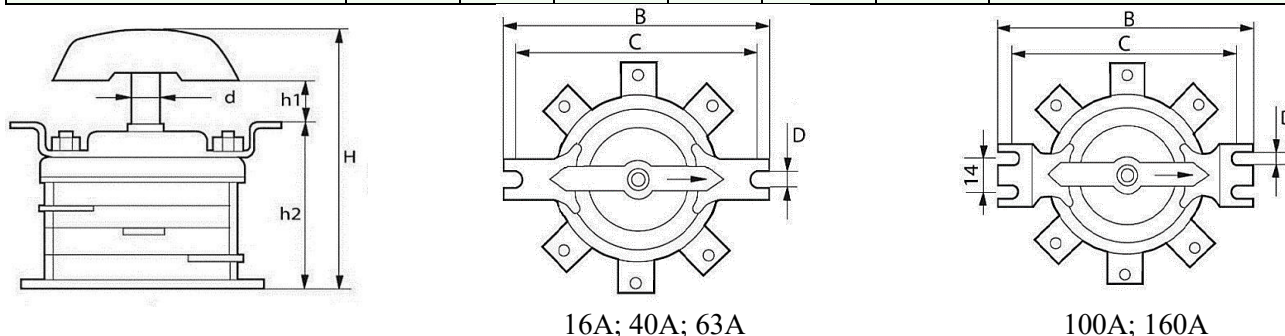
Габаритные и установочные размеры пакетных переключателей ПП. Исполнение 1. Степень защиты IP00. Способ крепления - передней скобой.
